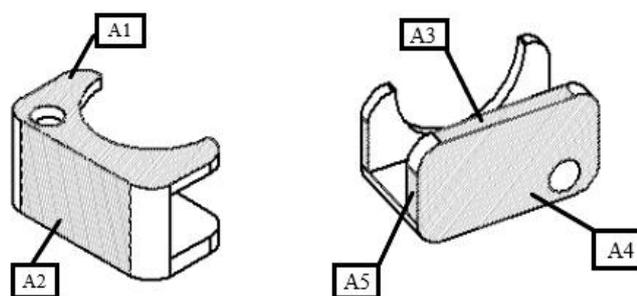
Posisi Pengukuran Radius Presisi Dimensi Objek Kompleks
